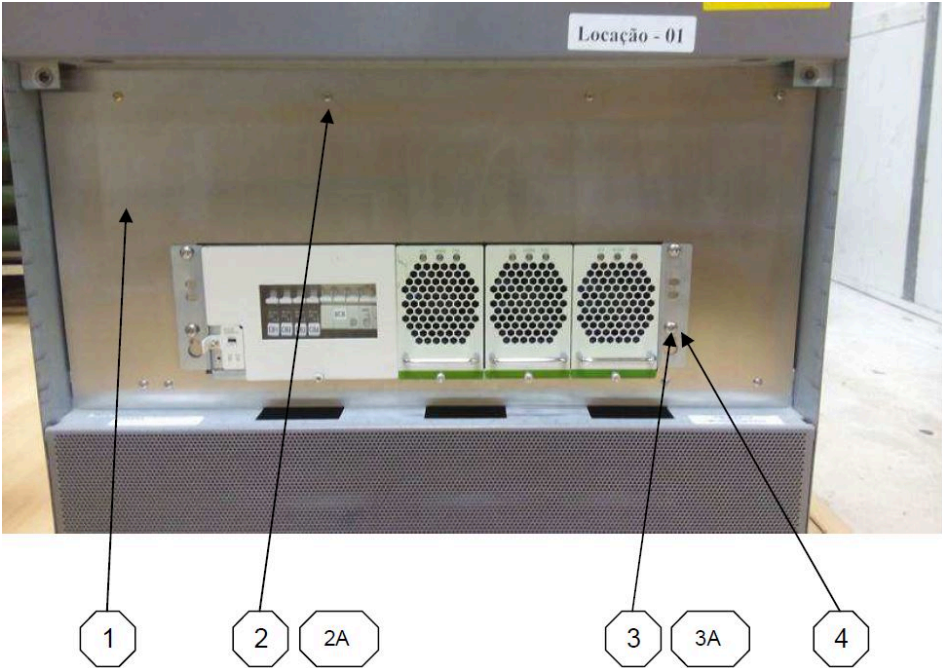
Kit C39165-A7080-B177-1: componentes que se utilizan en la parte frontal
